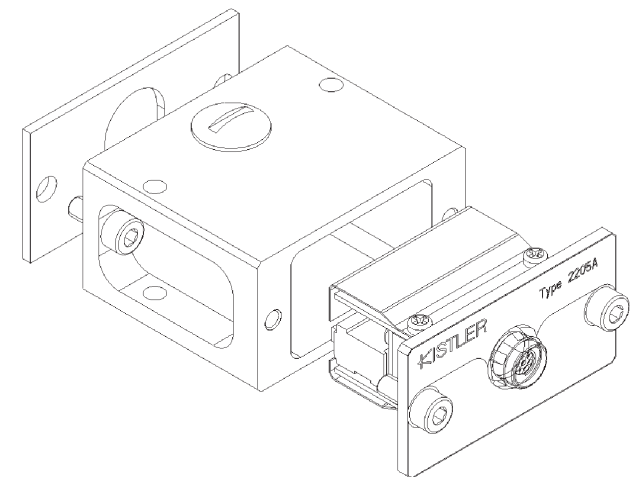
Einbau in Gehäuse für Montage am Spritzgießwerkzeug
